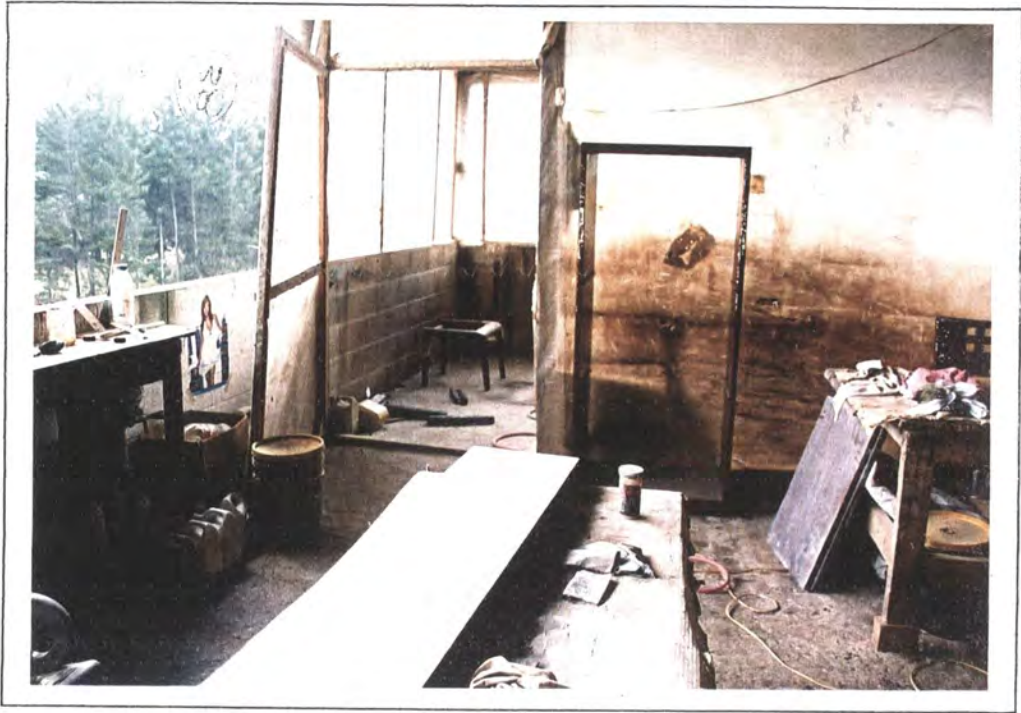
TERMINADO Y PINTURA / MUEBLES NAZARETH
